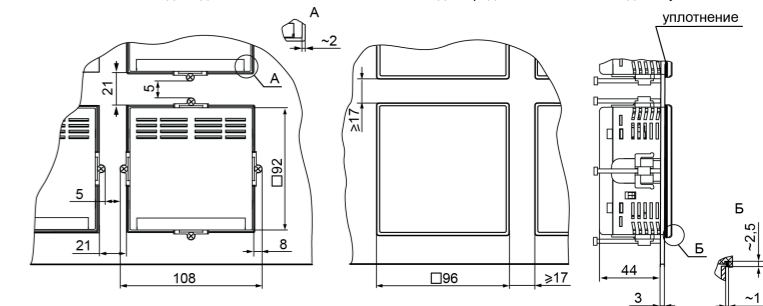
Габаритные размеры корпуса Щ1 и монтажного отверстия в щите
